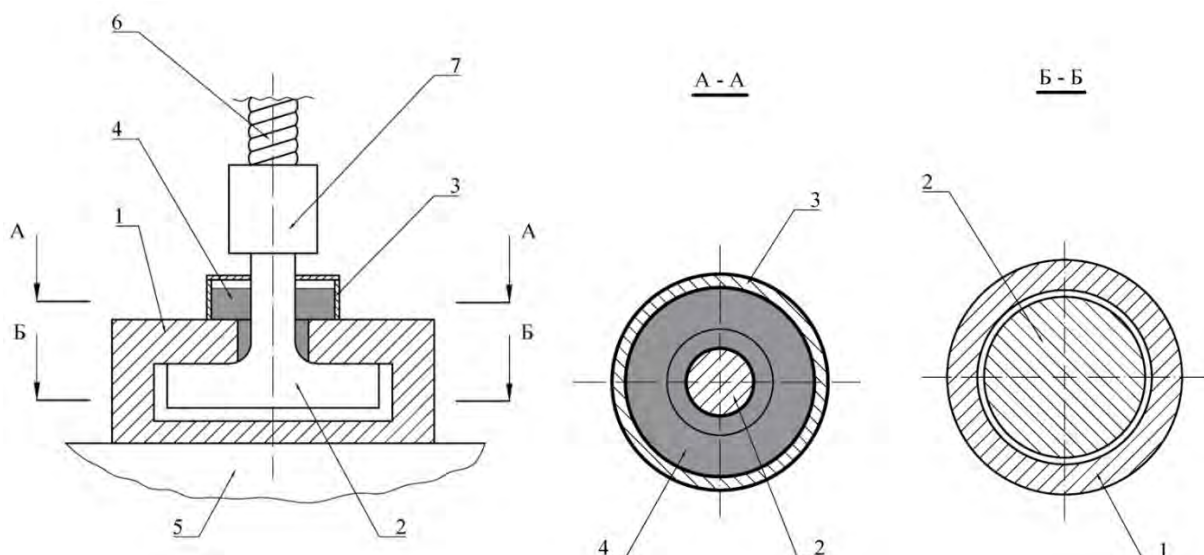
Устройство защиты тягового каната подъемной установки от закручивания: 1- корпус; 2 – ось; 3 – емкость; 4 – жидкое смазочное средство; 5 – подъемный сосуд; 6 – канат; 7 – устройство крепления каната
